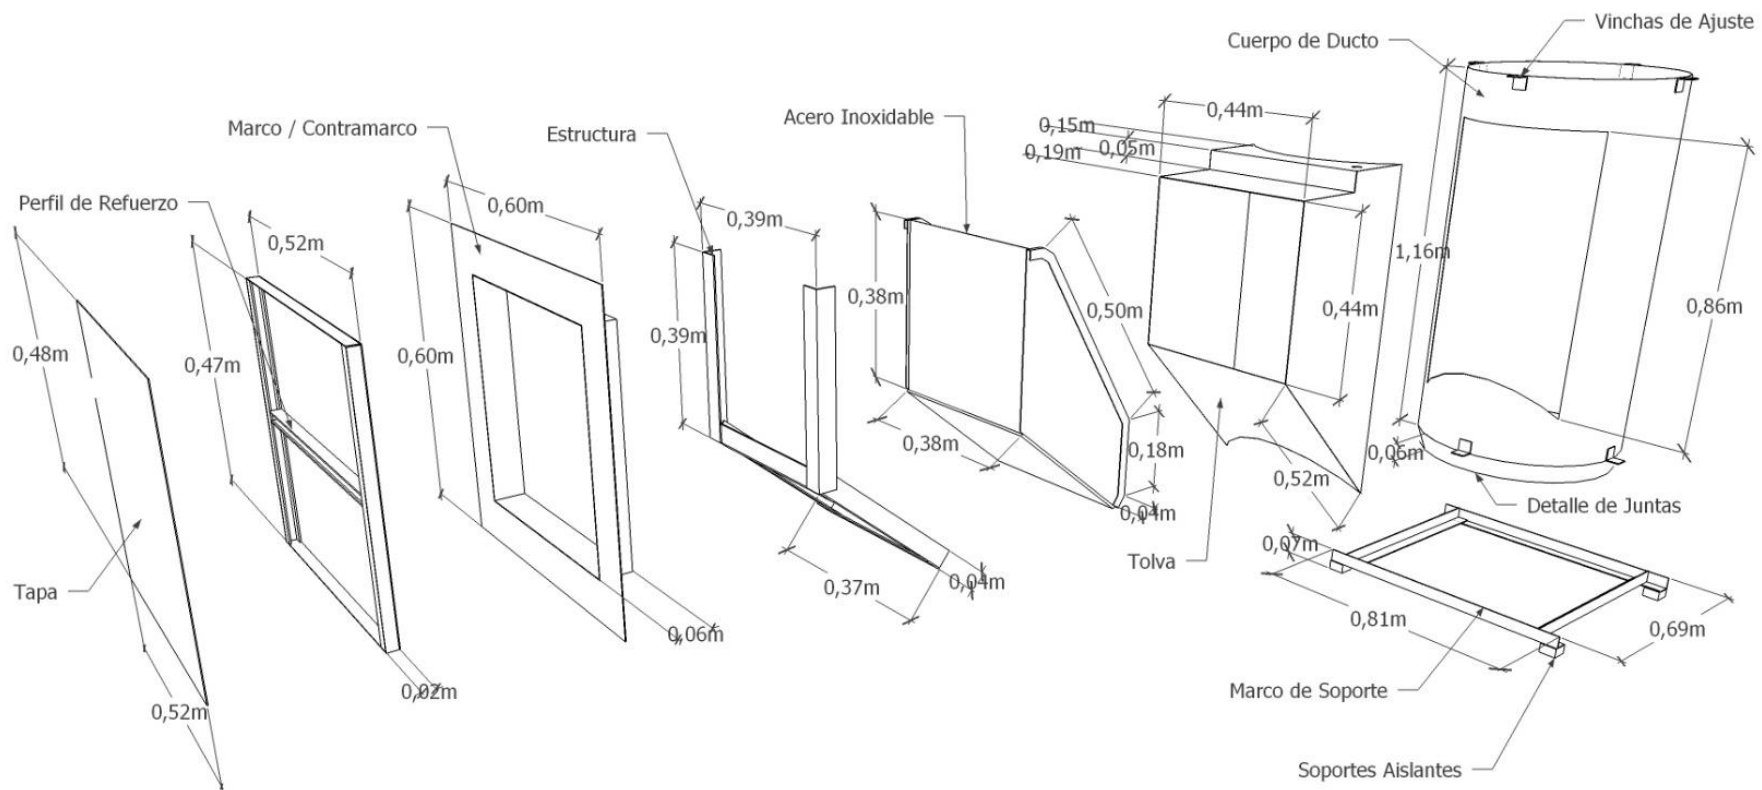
Ensamblaje de Puerta de Vertido y Fijación a la losa.
